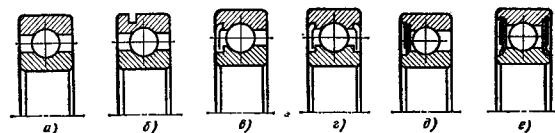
Шарикоподшипники радиальные однорядные типов: а — 00000; б — 50000; в — 60000; г — 80000; д — 160000; е — 180000
